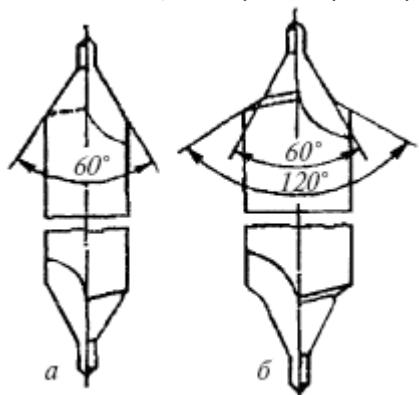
Центровочные сверла: а – обычные без предохранительного конуса; б – с предохранительным конусом
